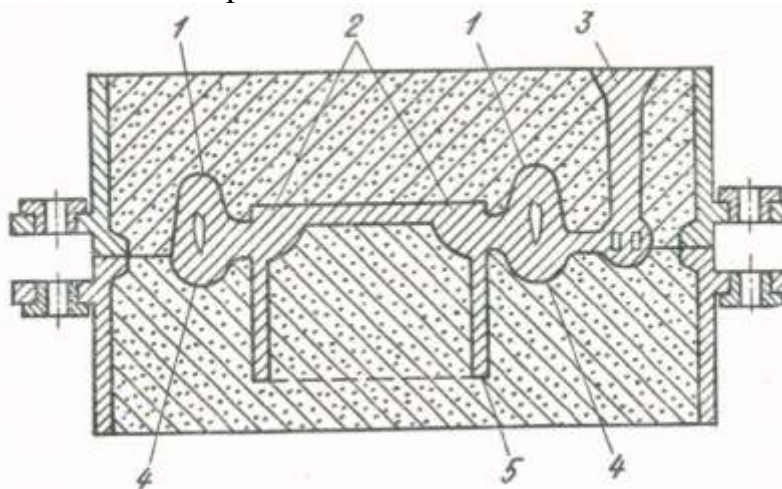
Форма для виливків з ковкого чавуну
